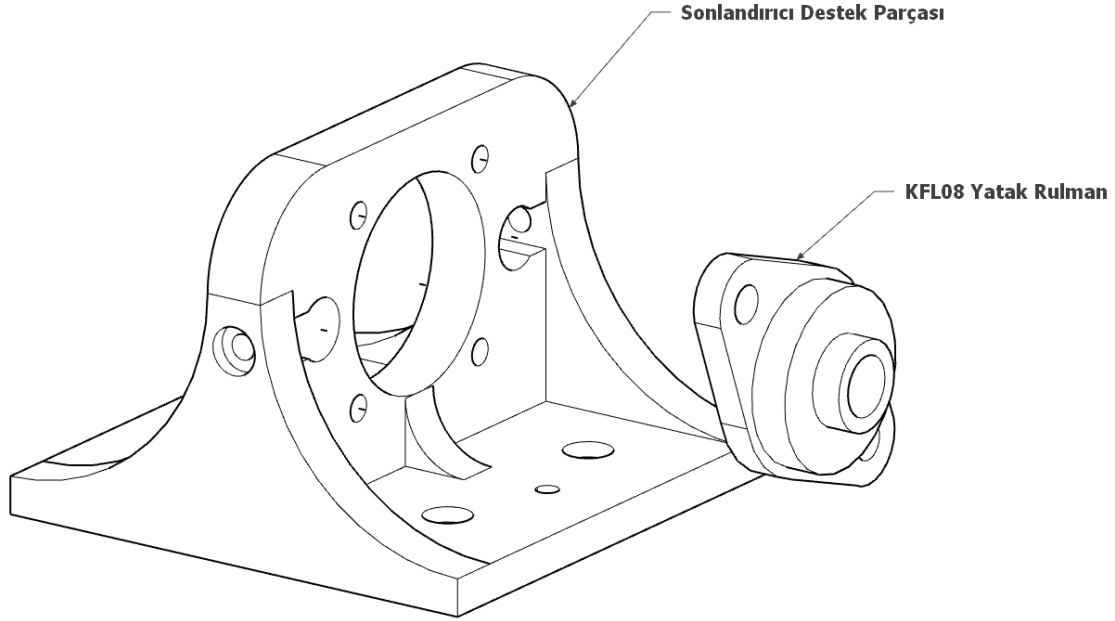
Motor yatağı parçasının diğer parçalar ile patlatılmış montaj görünümü
